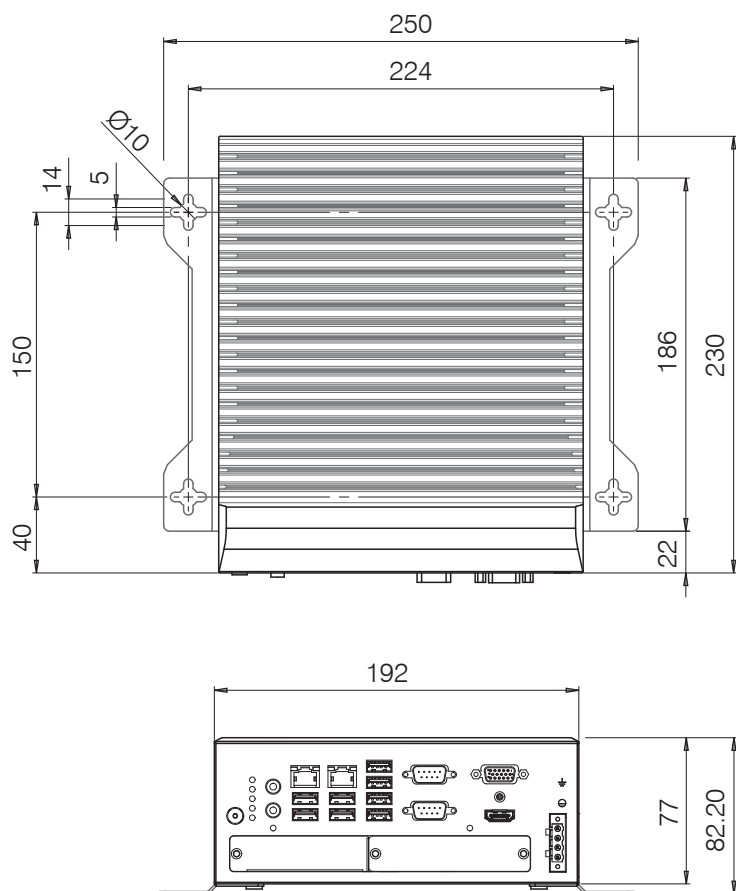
Maßzeichnung Controller SC2500 mit Montageadapter
